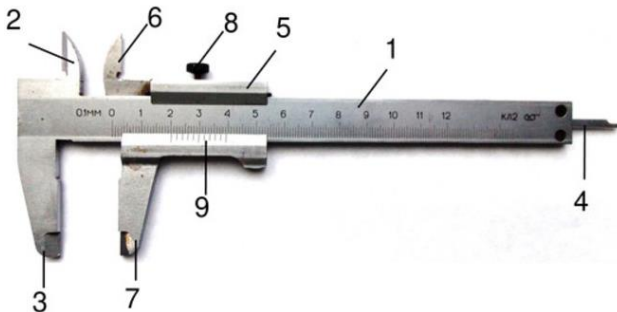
Штангенциркуль з ноніусом: 1 – штанга, 2 – нерухома верхня губка, 3- нерухома нижня губка, 4 – глибиномір, 5 – рамка, 6 – рухома верхня губка, 7 - рухома нижня губка, 8 – затискний гвинт, 9 - ноніус
